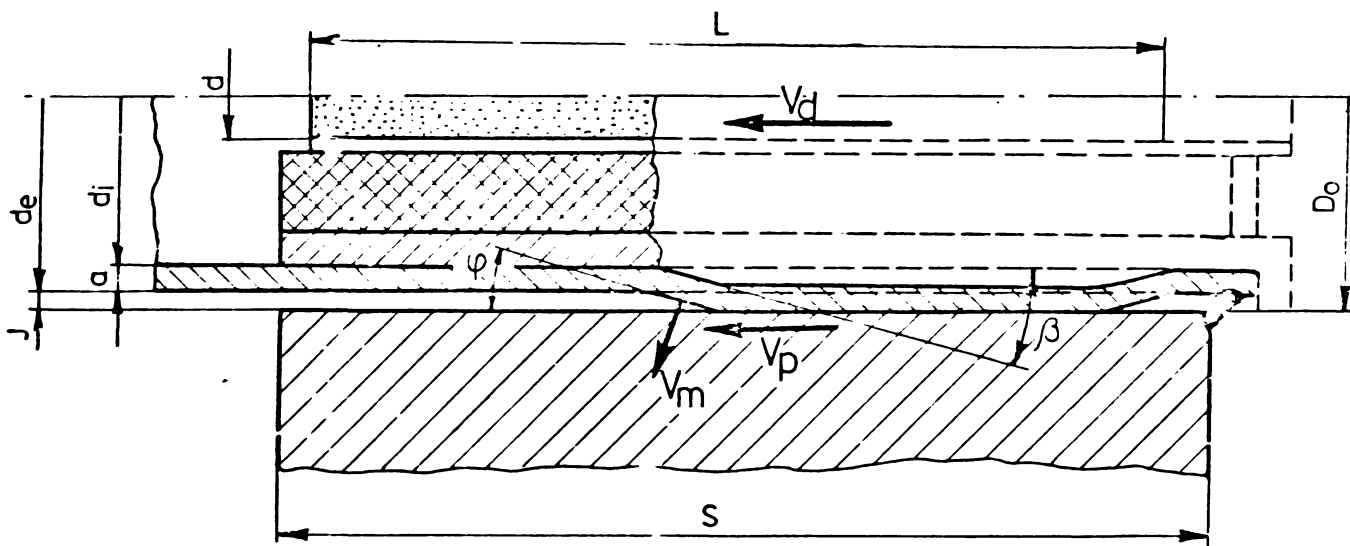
Parametrii la mandrinare-sudare prin explozie a țevilor la placa tubulară
